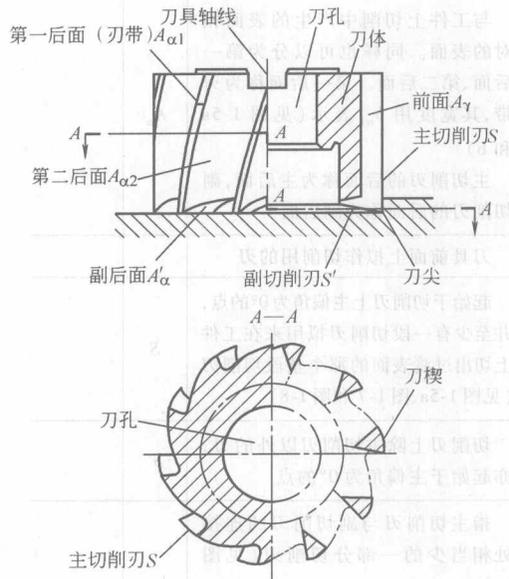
套式立铣刀切削部分上的切削刃和刀具表面
